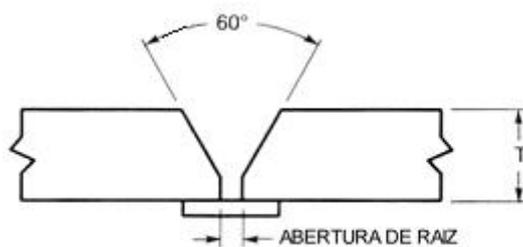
Junta a Tope Tubular, Con Respaldo – Calificación de Soldador
